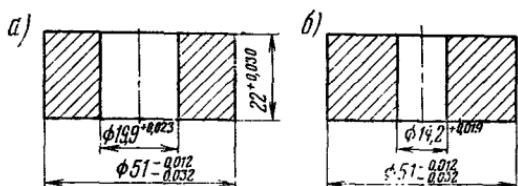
Кондукторные втулки для запрессовки осей в корпус вспомогательного насоса:
